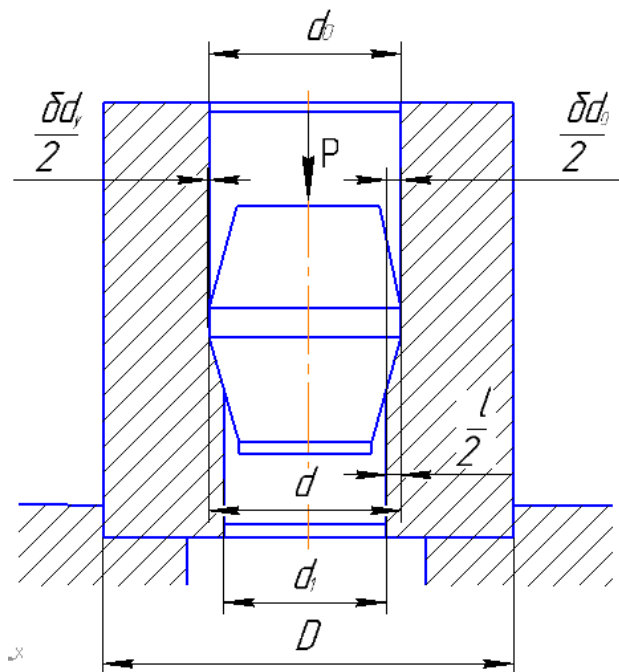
Схема дорнування втулки та позначення розрахункових величин:
